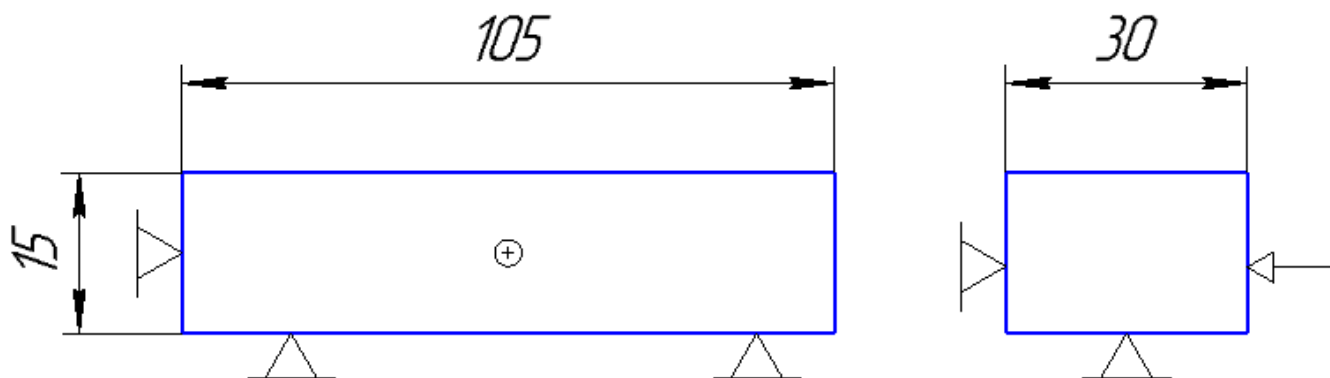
Схема базування та кріплення деталі на операції 005 Фрезерна з ЧПК
